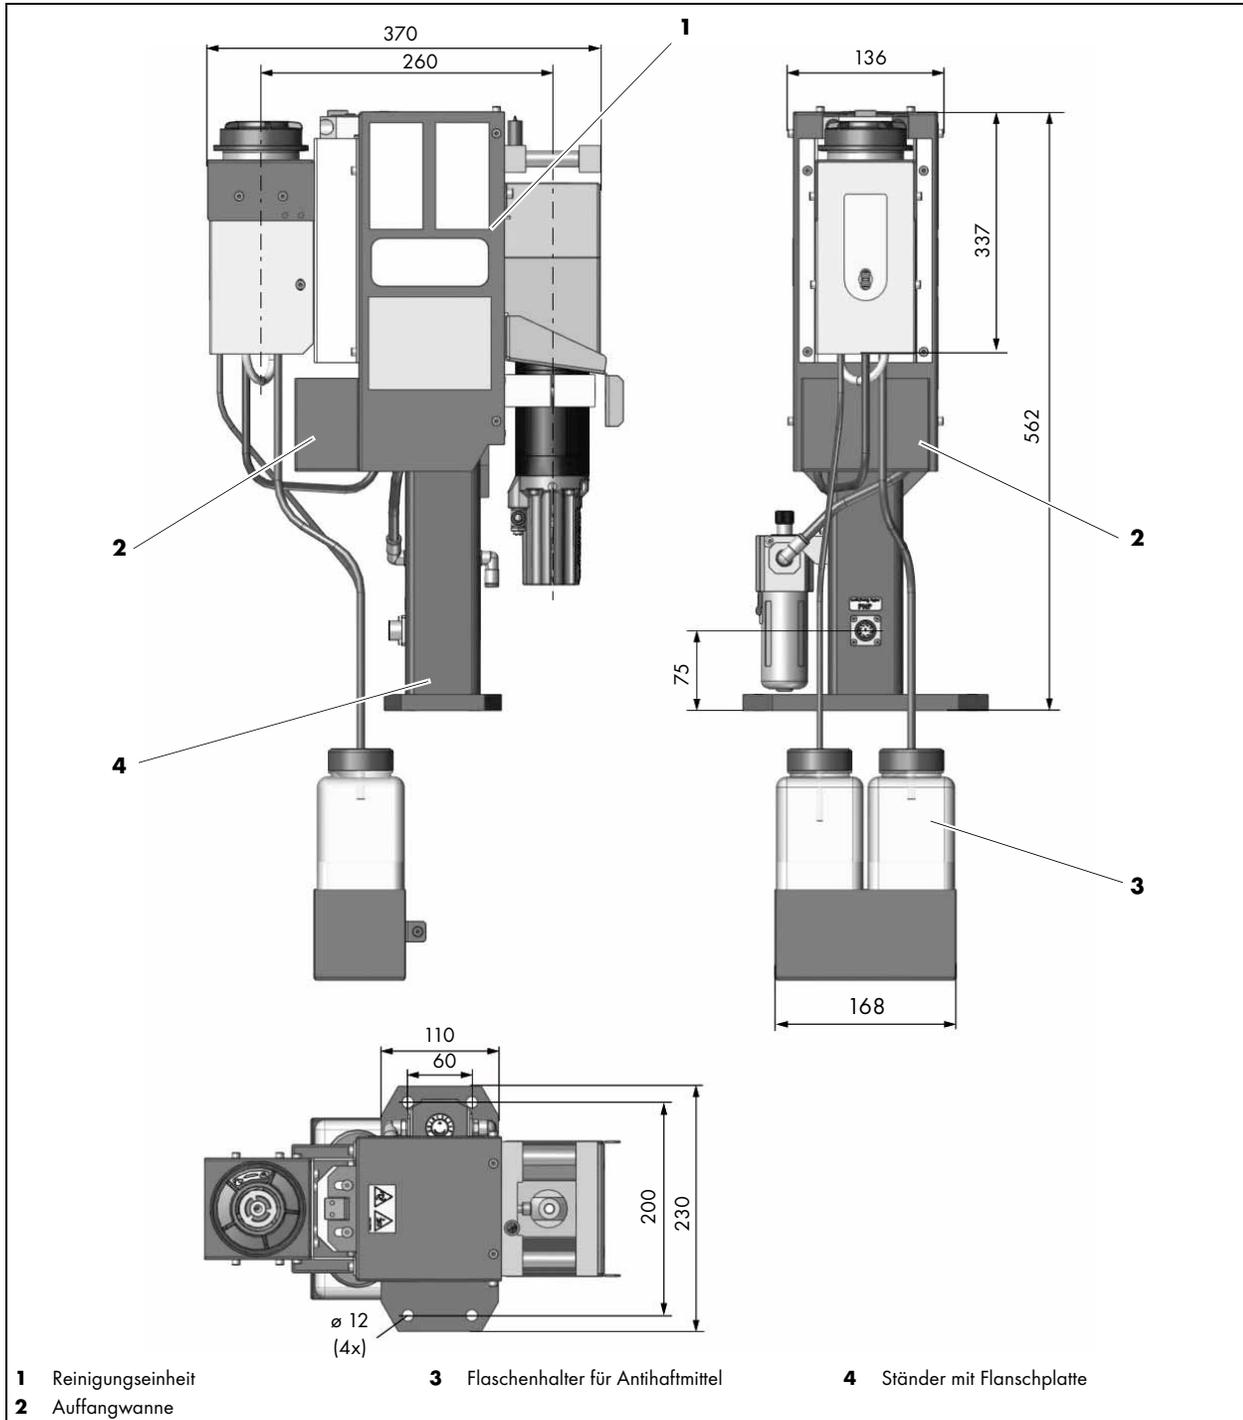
Technische Daten - Ausführung mit kurzem Geräteständer
